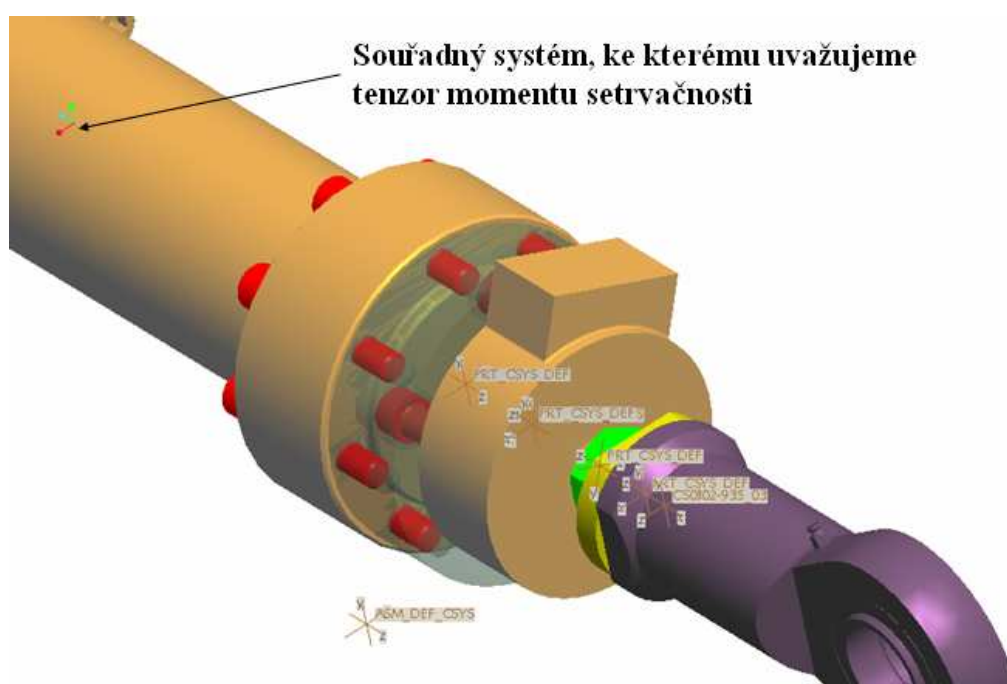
Setrvačné hmoty horní části uložení zapsané do Adamsu
